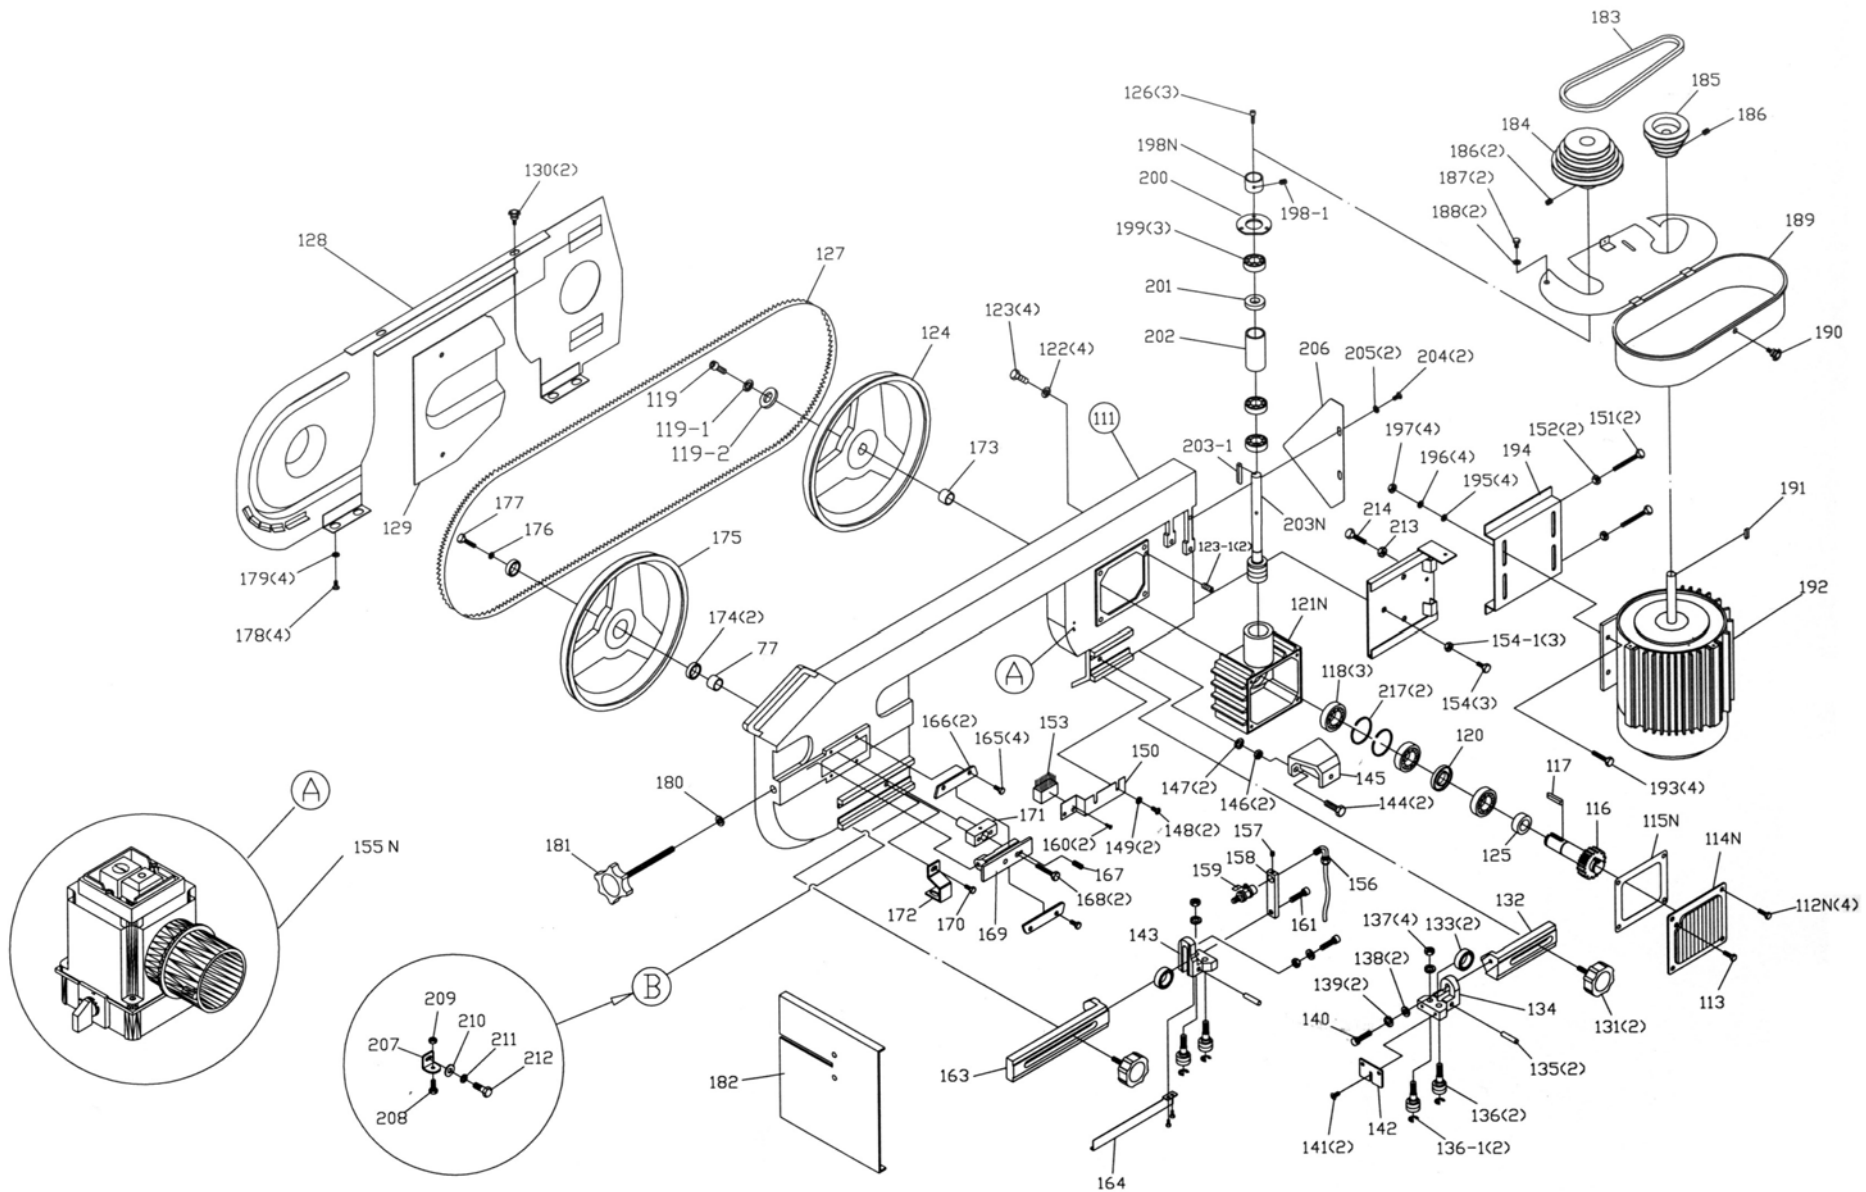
Explosionszeichnung 2 - Explosion drawing 2 S181
